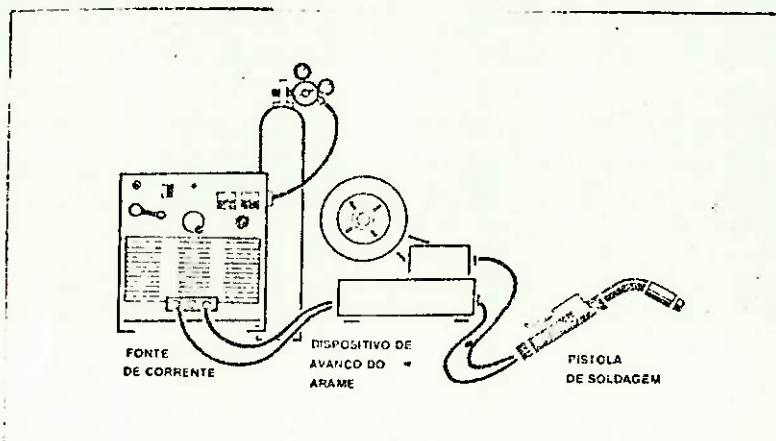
EQUIPAMENTO PARA SOLDAGEM MIG/MAG
